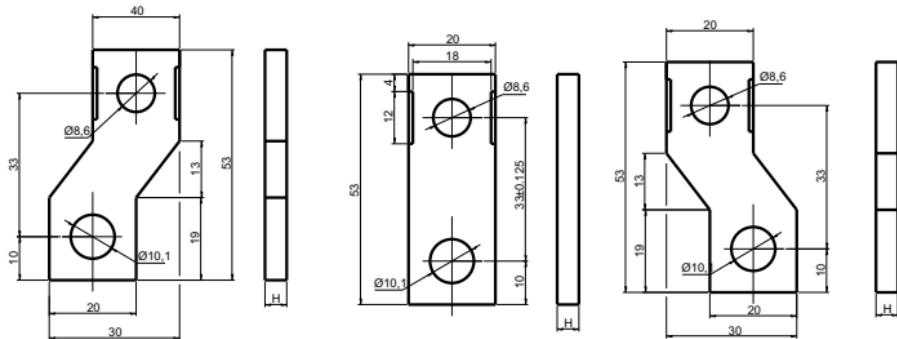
Габаритные и установочные размеры наконечников-переходников для выключателей ВА88-32, ВА88-33 и ВА88-35 /
